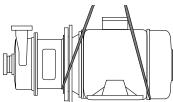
Transporte del grupo motobomba (en motores ≥ 5,5 kW)
